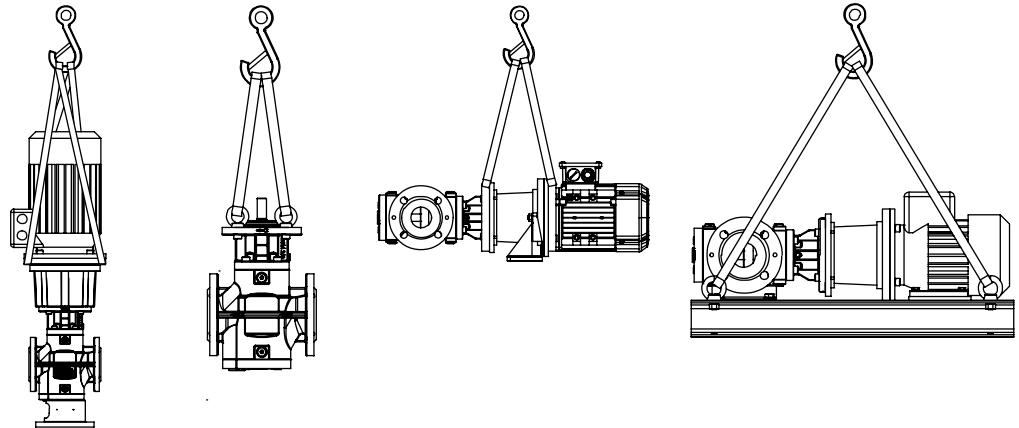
Befestigung Hebezeug - Prinzipbilder
